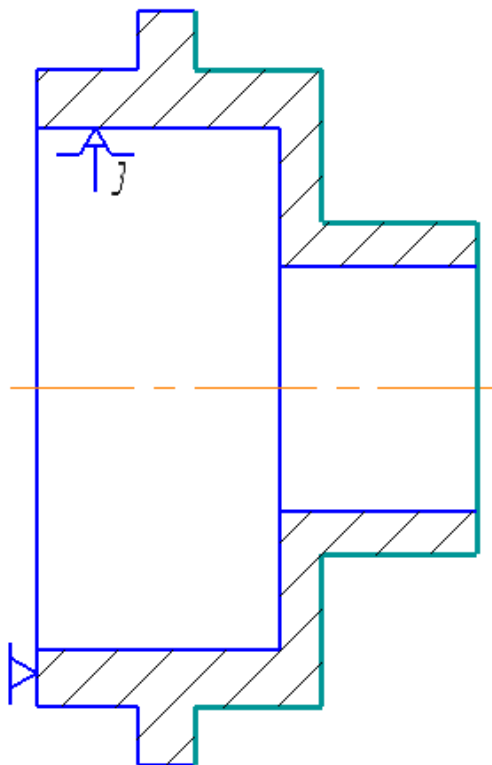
Схема базирования заготовки на 010 Токарной операции с ЧПУ
